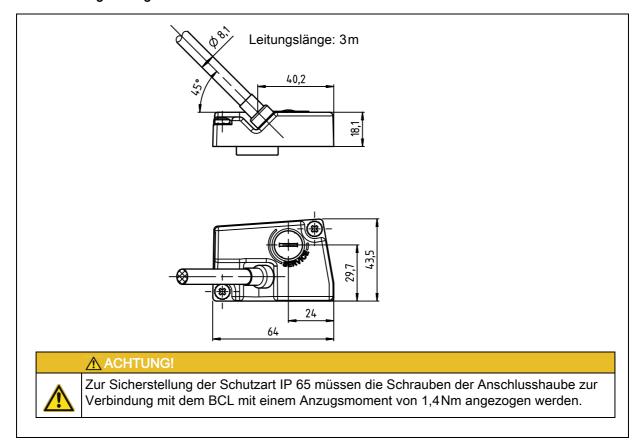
Maßzeichnung Leitungshaube KB 301-3000
